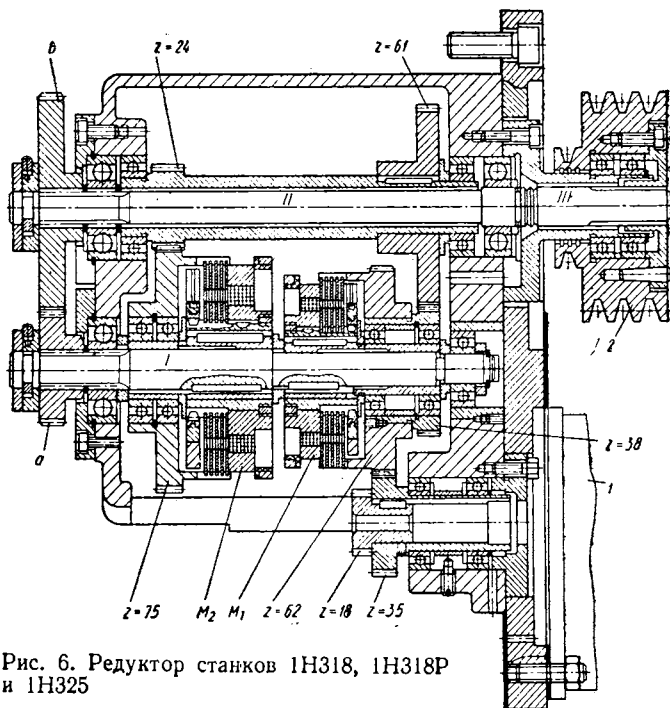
Редуктор станков 1Н318, 1Н318Р и 1Н325
